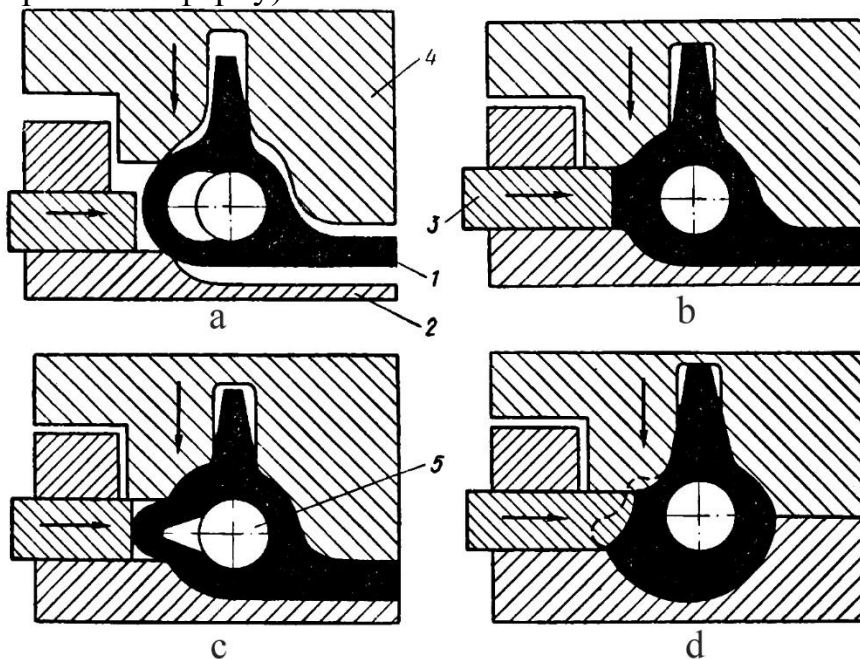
Схема формування вушок ланок гусениць пластичним деформуванням: а, б, с, d – послідовність деформування у гарячому стані; 1 – ланка гусениці; 2, 4 – корпус матриці; 3 – прес; 4 – корпус
